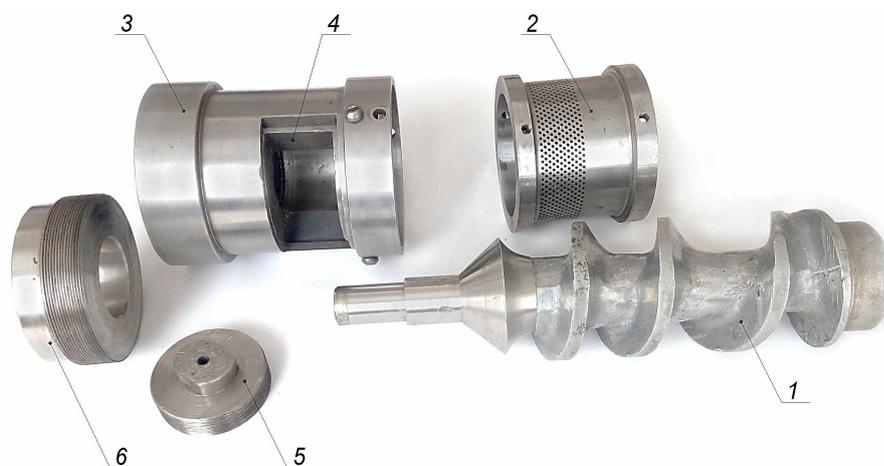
Внешний вид узла сепаратора в разобранном виде: 1 – шнек нагнетающего типа; 2 – перфорированная втулка (сепаратор); 3 – опорный корпус; 4 – запирающий конус (клапан); 5, 6 – винты регулировки кольцевого зазора
